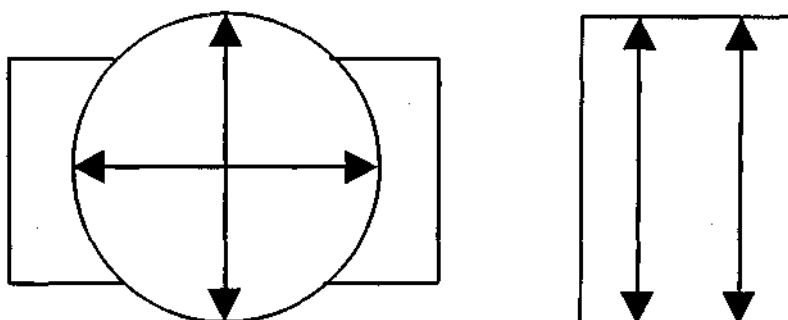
Схема виміру внутрішнього діаметра корпусу букси
